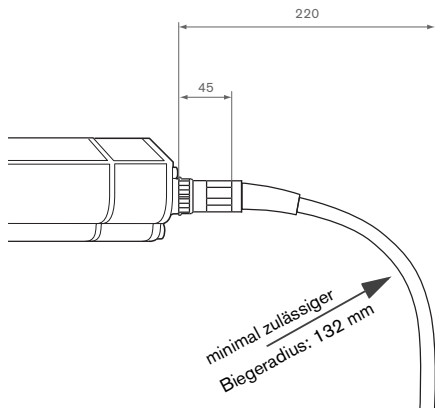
Mindestbiegeradius der Anschlussleitung Schraubspindel
